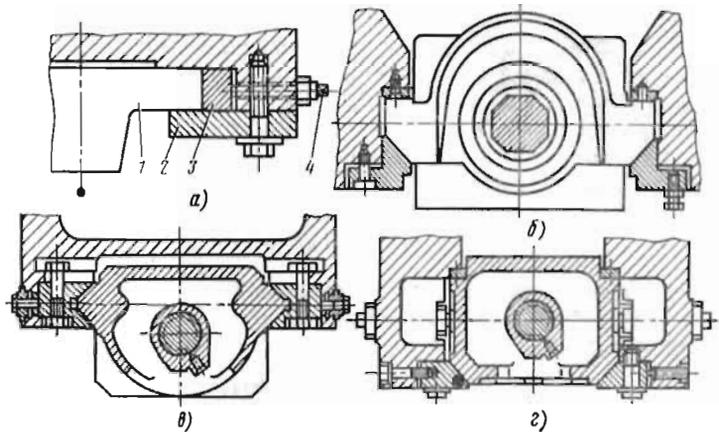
Сечения ползунов и направляющих открытых однокривошипных прессов: а — плоские: 1 — ползун; 2 — наружная направляющая; 3 — регулировочный клин; 4 — установочный винт; б — трапециевидные: в — треугольные; г — корычатога сечения
